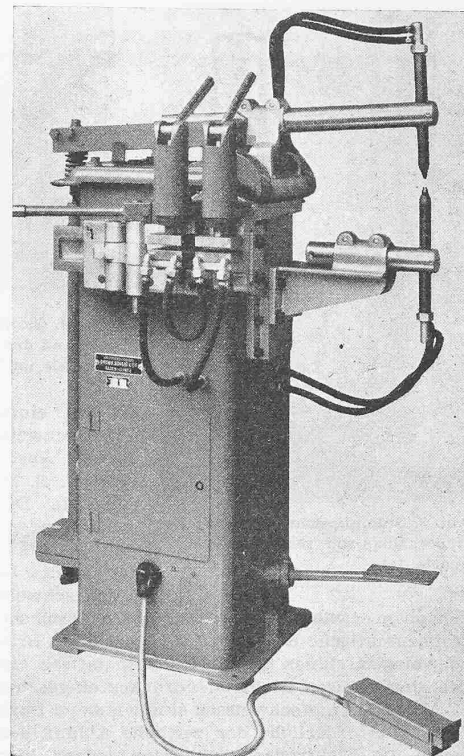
Punktschweissmaschine von 25 kVA
